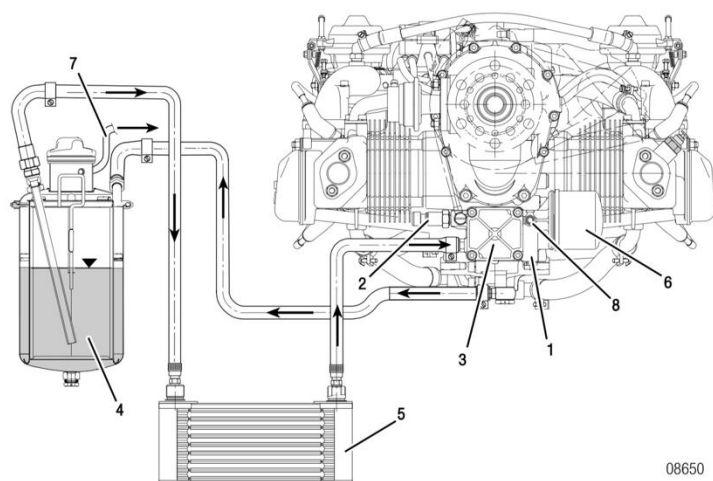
chladicí systém motoru Rotax 912 ULS, zdroj: [5]
